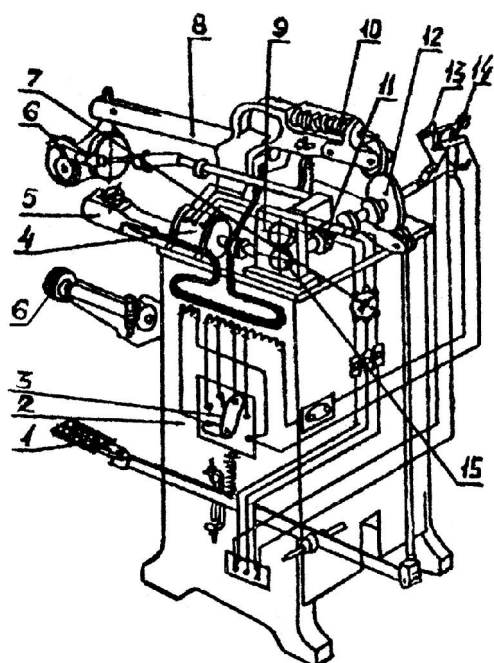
Схема машины для контактной точечной сварки МТ – 601.
